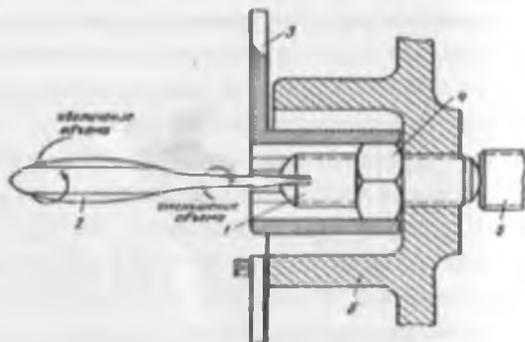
Тарировка поршневого счетчика жидкости: 1 – регулировочный винт; 2 – отверстие; 3 – специальный ключ; 4 – гайка М10; 5 – кулиса; 6 – боковая крышка
